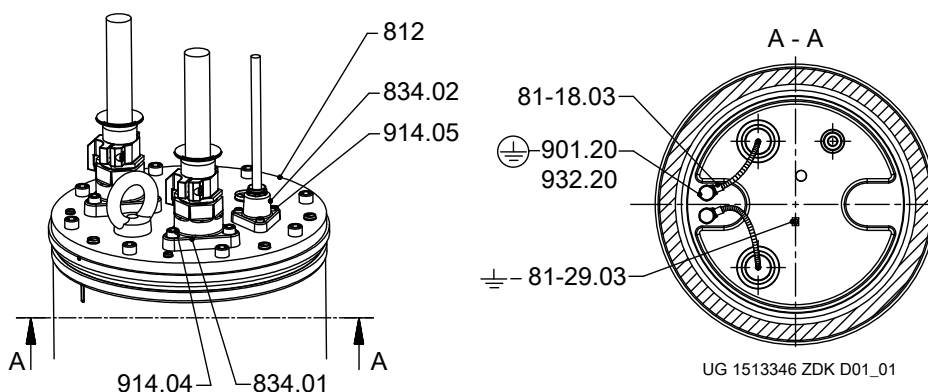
Демонтаж кабеля подсоединения и кабельного ввода
